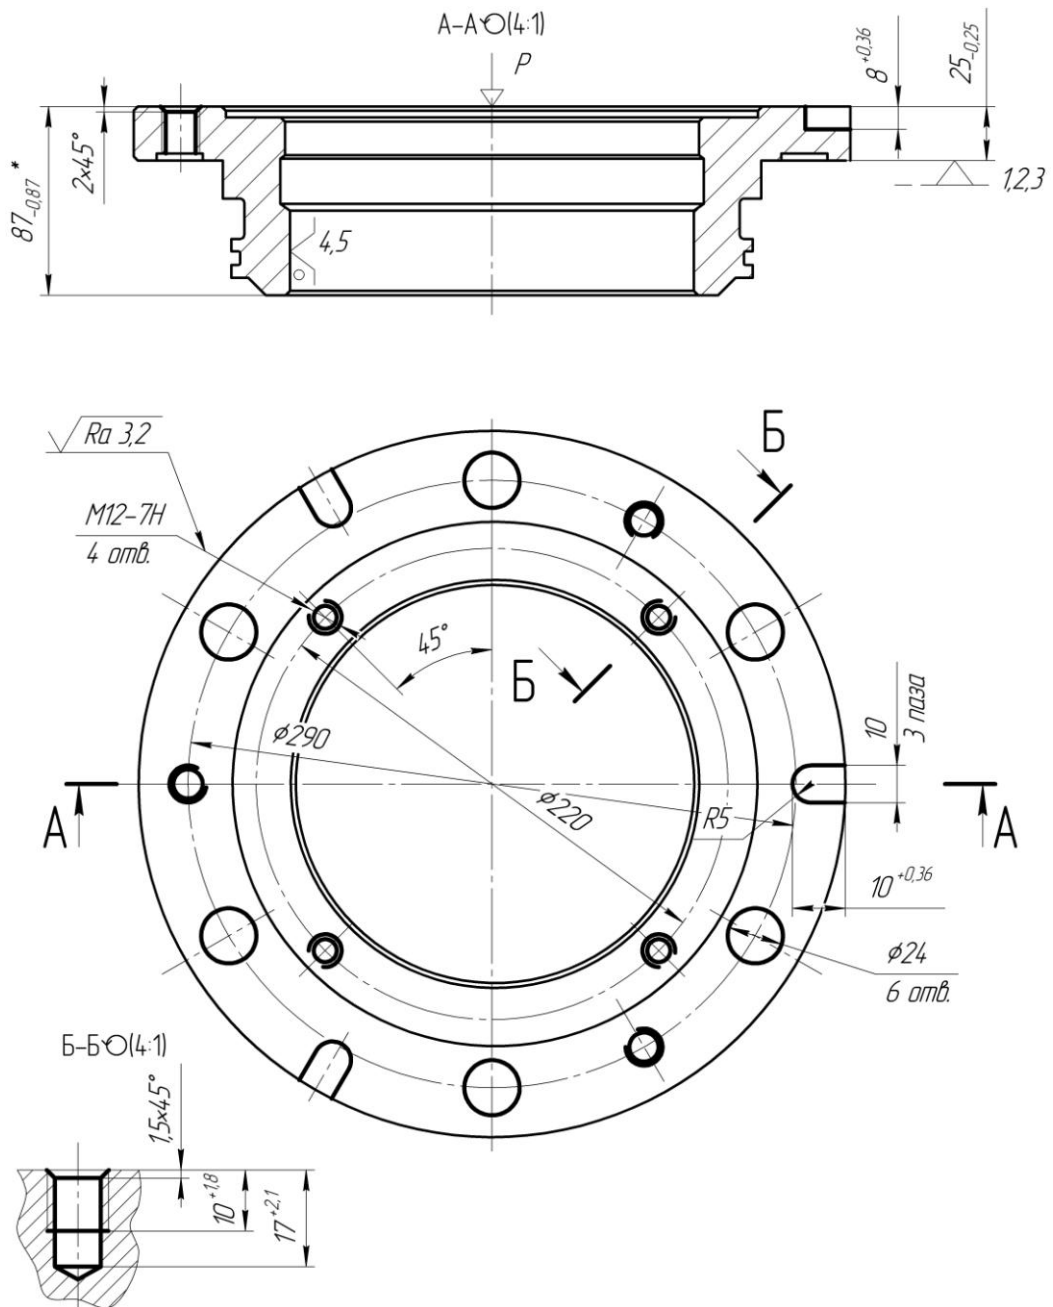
Схема базирования заготовки на вертикально-фрезерной с ЧПУ операции (второй вариант)
